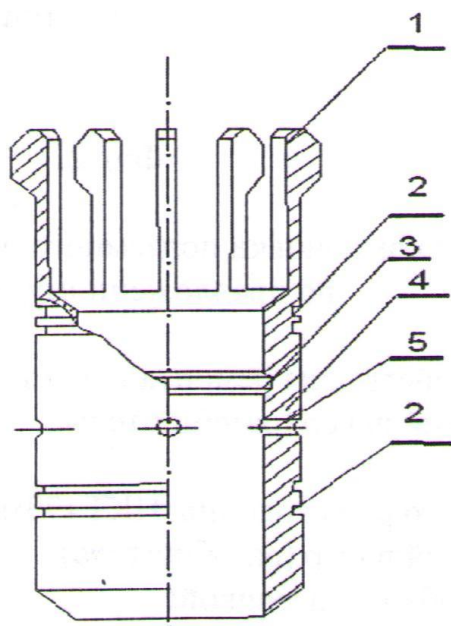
Извлекаемый забойный иштуцер (дополнительно введенный): 1 - упругий замковый фиксатор; 2 - канавки для уплотнительных колец; 3 - захватное место для работы с канатной техникой; 4 - корпус иштуцера; 5 - калиброванные отверстия иштуцера
